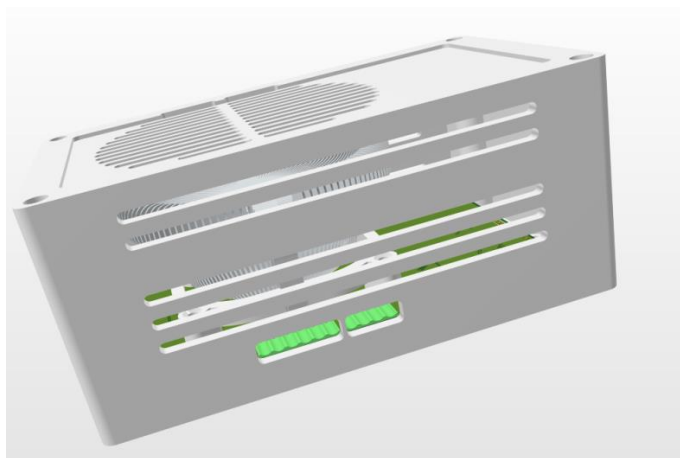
3D модель корпуса C7020044 с кулером и доработкой
